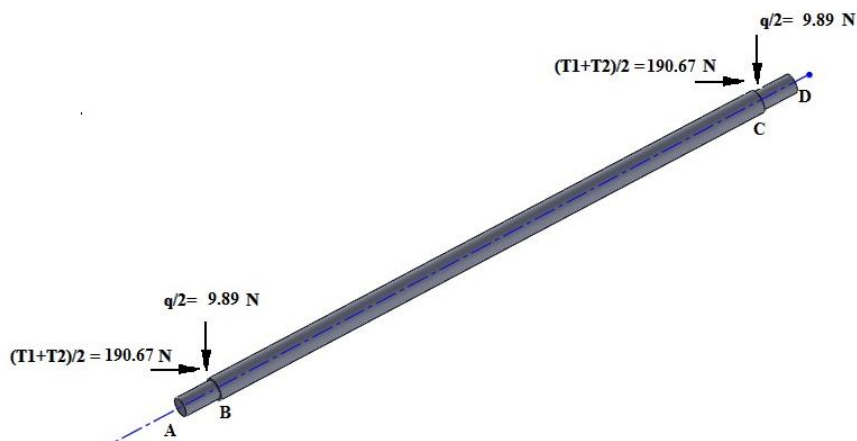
Fuerzas que actúan en los rodamientos del eje del tambor de cola
